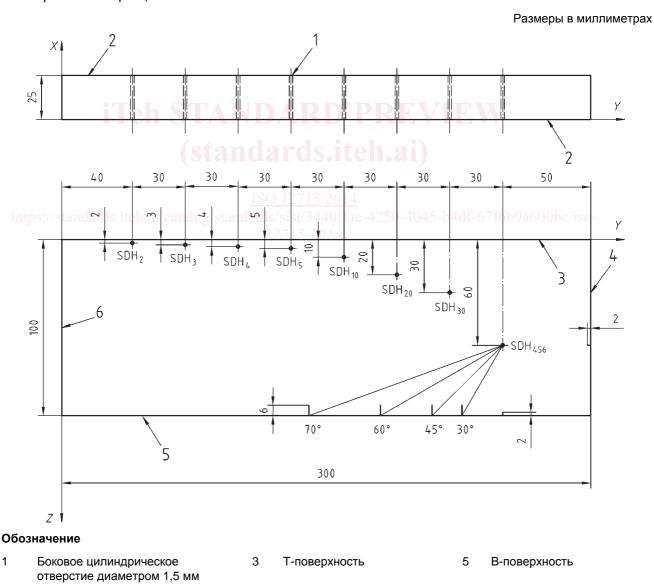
Образец с боковыми цилиндрическими отверстиями (SDH)
